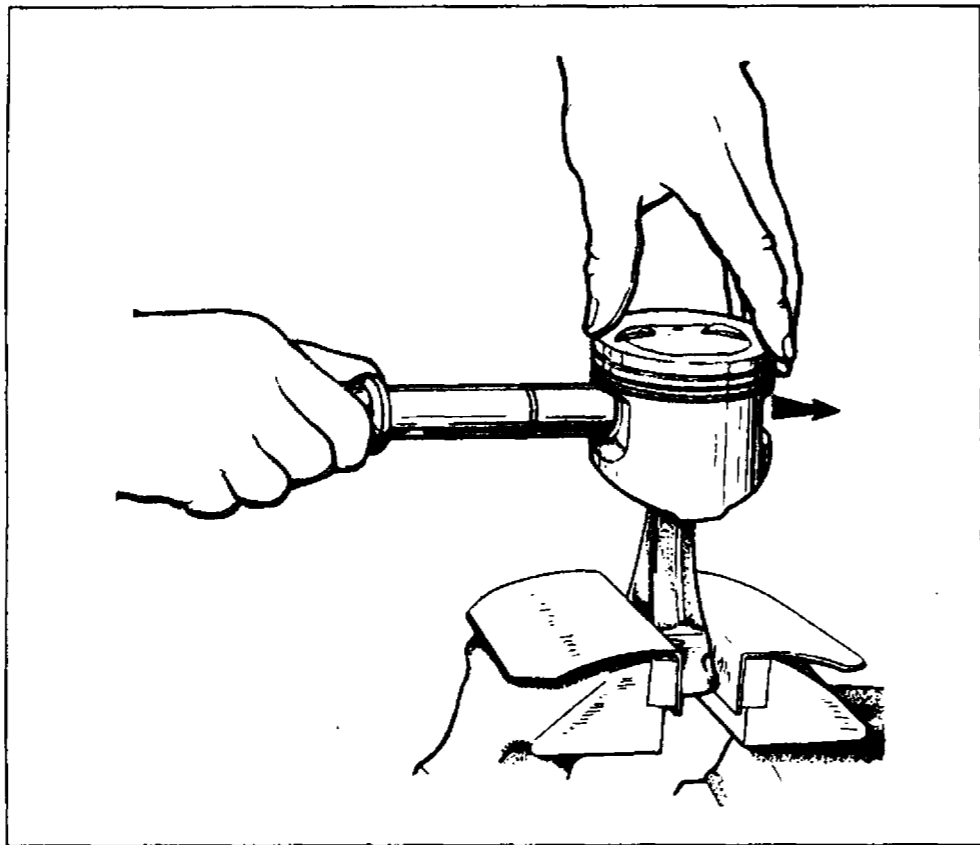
Запрессовка поршневого пальца в верхнюю головку шатуна. Поршень должен опираться на головку шатуна в направлении, указанном стрелкой
